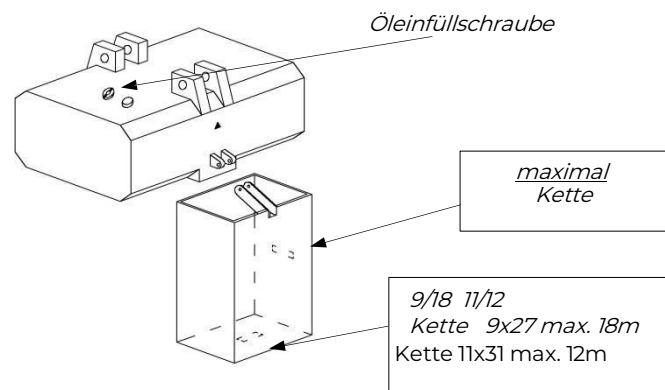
Kettenspeicherbefestigung und Öleinfüllschraube
